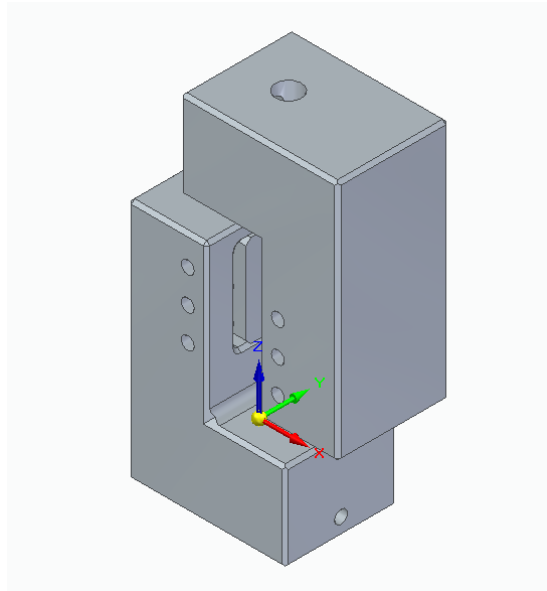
Primer diseño del utillaje para ensayo de Arcan
